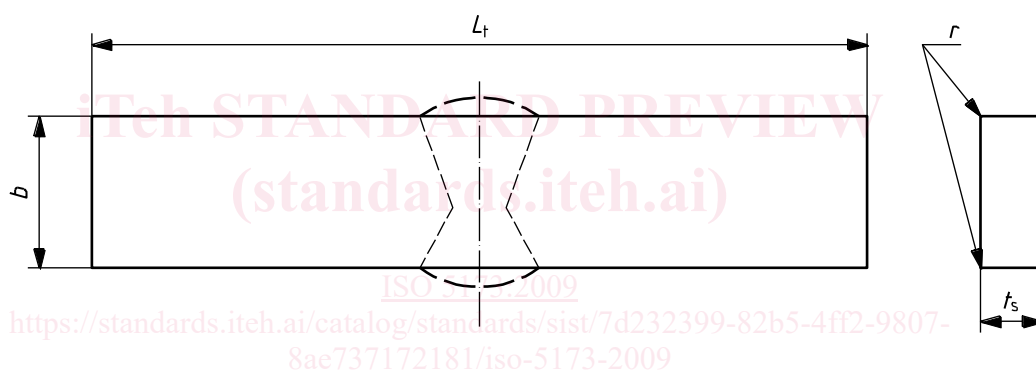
Поперечный образец для испытаний стыковых сварных швов на загиб с растяжением боковой стороны (SBB)
